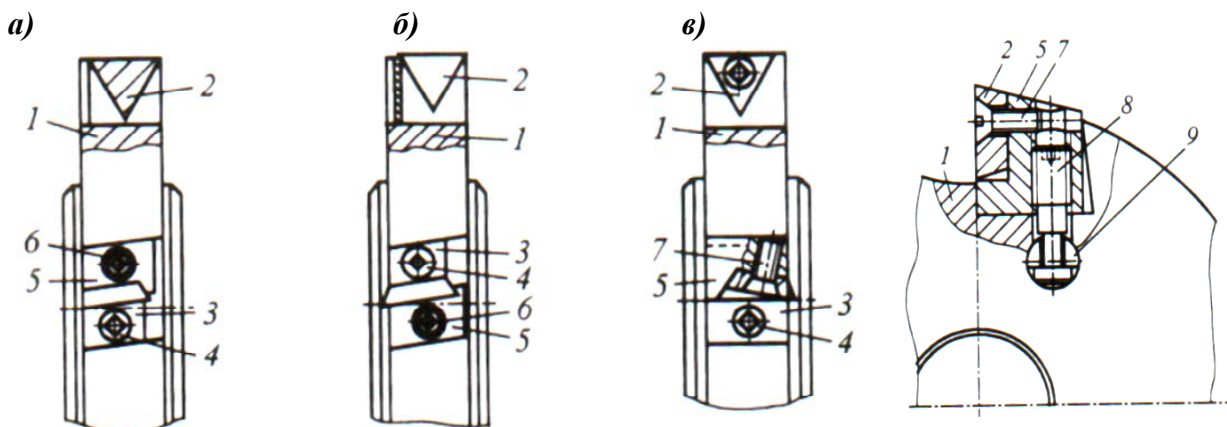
Основные конструкции сборных дисковых фрез с вкладышами для крепления СМП трехгранной формы
